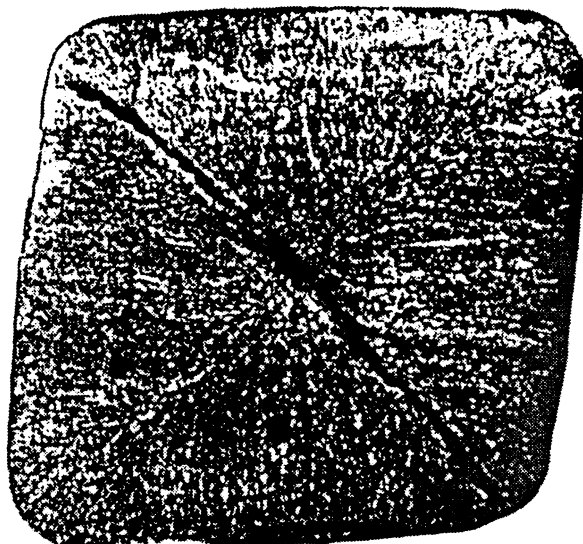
Вид крупной внутренней трещины в сортовой заготовке, расположенной вдоль диагонали между тупыми углами поперечного сечения по данным [6]
